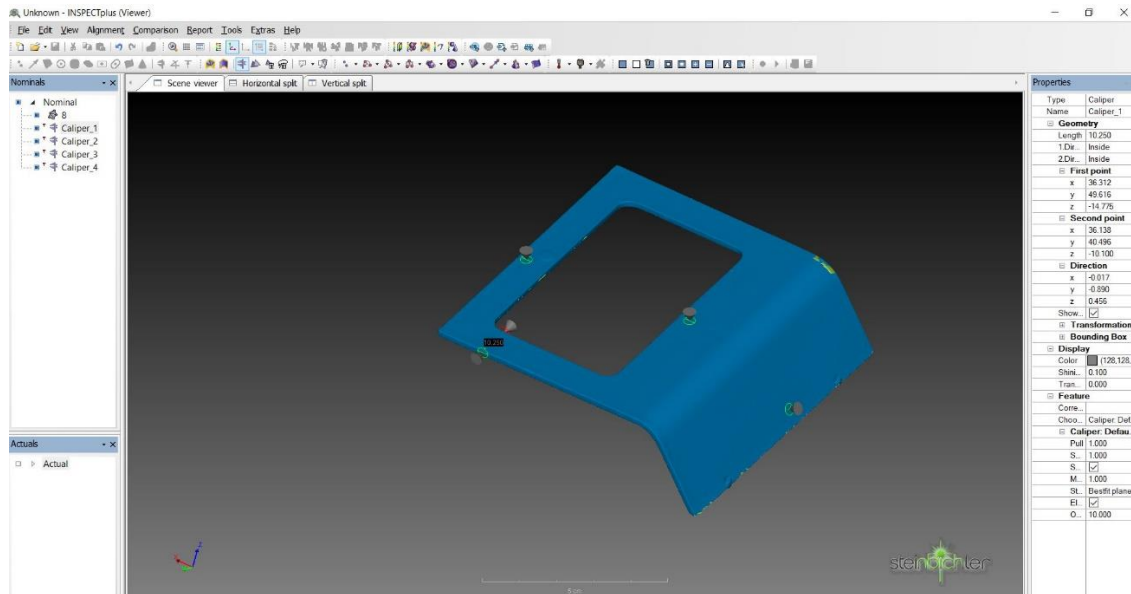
Controlo dimensional de uma das moldações no *INSPECTplus
